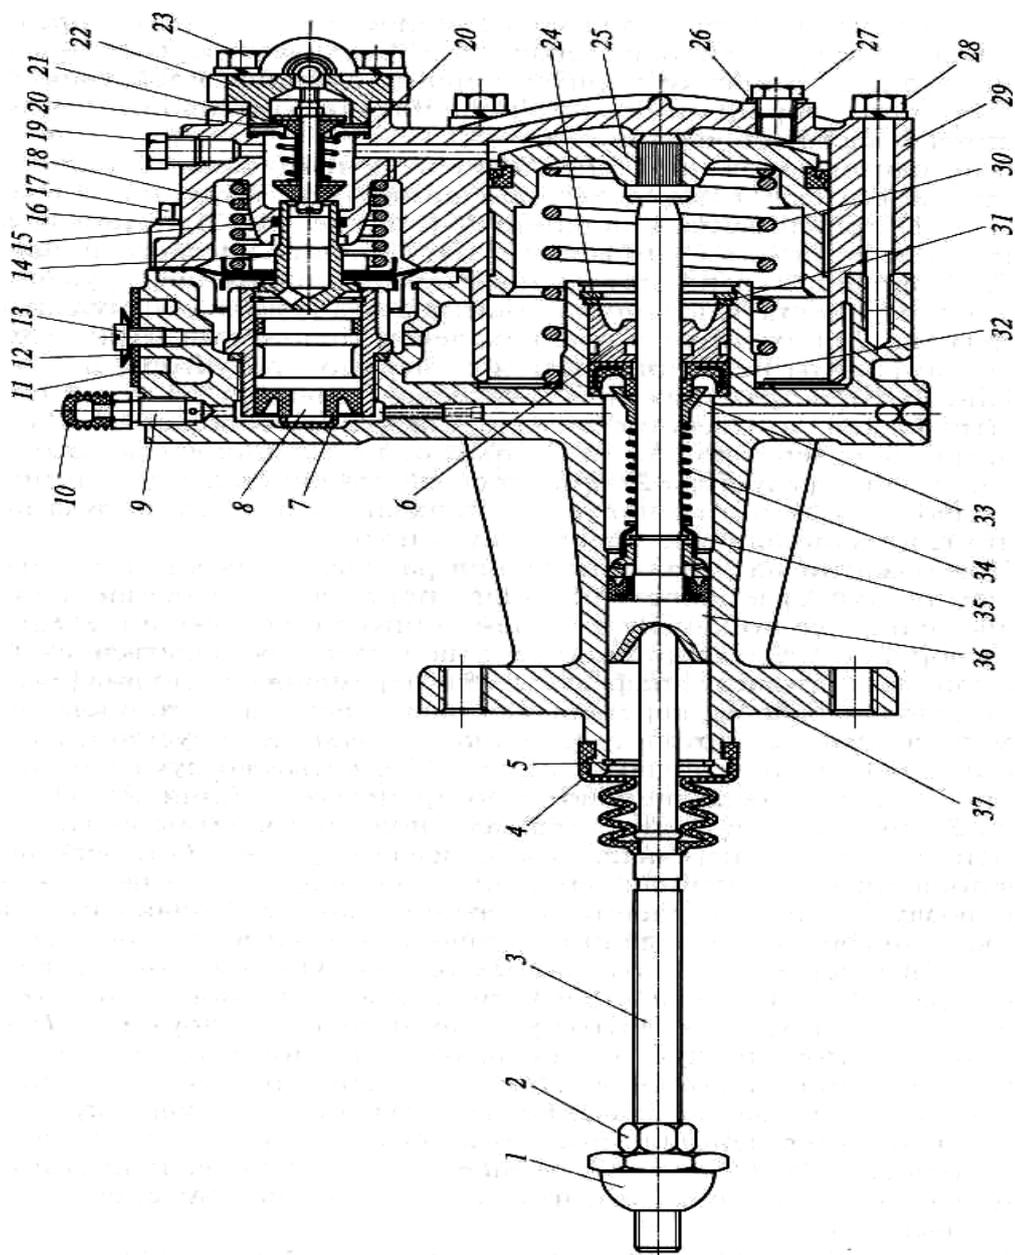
Пневмогидравлический усилитель привода сцепления: 1-гайка сферическая толкателя; 2 — контргайка; 3 — толкатель поршня; 4 — защитный чехол; 5 — стопорное кольцо; 6 — уплотнение поршня; 7, 15 — уплотнительные кольца; 8 — следящий поршень; 9 — перепускной клапан; 10 — колпачок; 11 — уплотнитель выпускного отверстия; 12 — крышка выпускного отверстия; 13 — винт; 14 — седло диафрагмы; 16 — пружинная шайба; 17 — болт М8*35; 18 — пружина диафрагмы; 19, 27 — пробки; 20 — седло; 21 — клапан редуктора; 22 — крышка подвода воздуха; 23 — болт М8 х 25; 24 — упорное кольцо; 25 — поршень пневматический; 26 — прокладка; 28 — болт М8*70; 29 — передний корпус; 30 — пружина пневматического поршня; 31 — шайба; 32 — манжета; 33 — втулка распорная; 34 — распорная пружина; 35 — втулка; 36 — поршень выключения сцепления; 37 — задний корпус.
